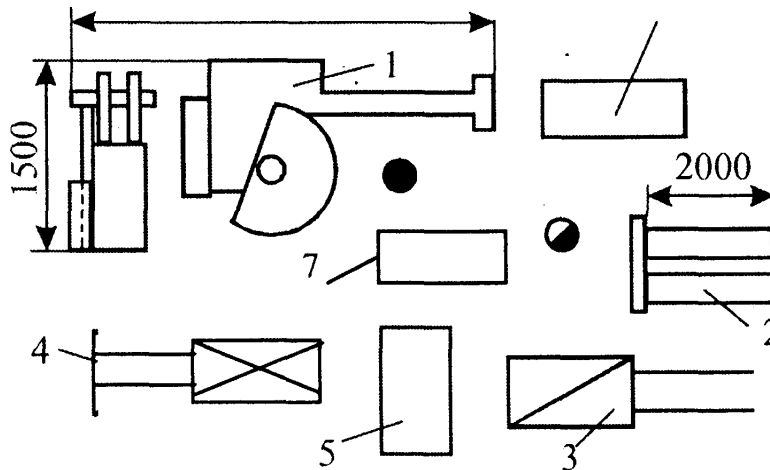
Схема організації робочого місця біля горизонтального гнутакого верстата: 1 - гнутакий верстат; 2 - пропарочні котли; 3,4 - заготовки до і після гнуття; 5,6 - місця з запасними шинами та шаблонами; 7 - робочий стіл для накладання шини
